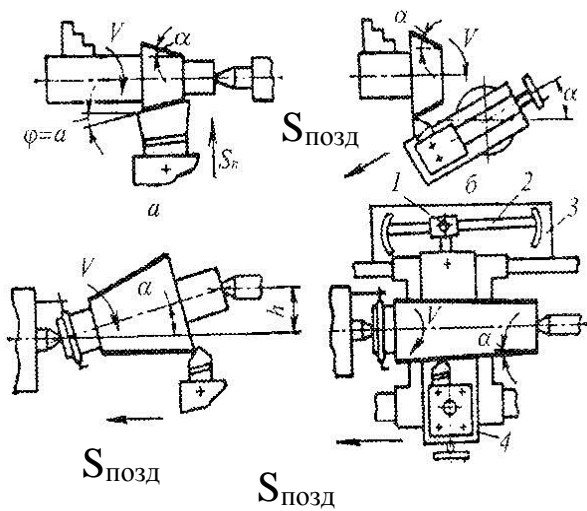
Схеми обточування зовнішніх конічних поверхонь на токарно-гвинторізних верстатах
